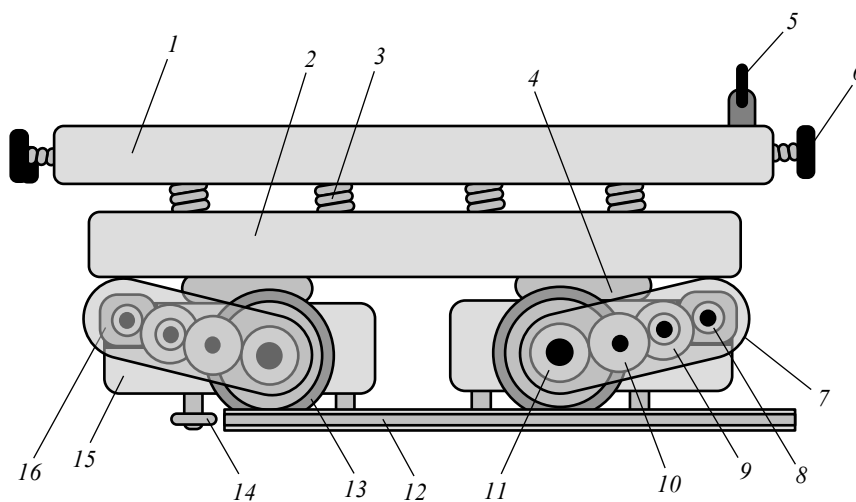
Злитковоз: 1 — платформа; 2 — плита; 3 — пружинний амортизатор; 4 — підшипник; 5 — підвод електроенергії; 6 — буфер; 7 — редуктор; 8, 9, 10, 11 — зубчасті колеса; 12 — рейсь; 13 — колесо; 14 — напрямний ролик; 15 — ходова тележка; 16 — електродвигун
